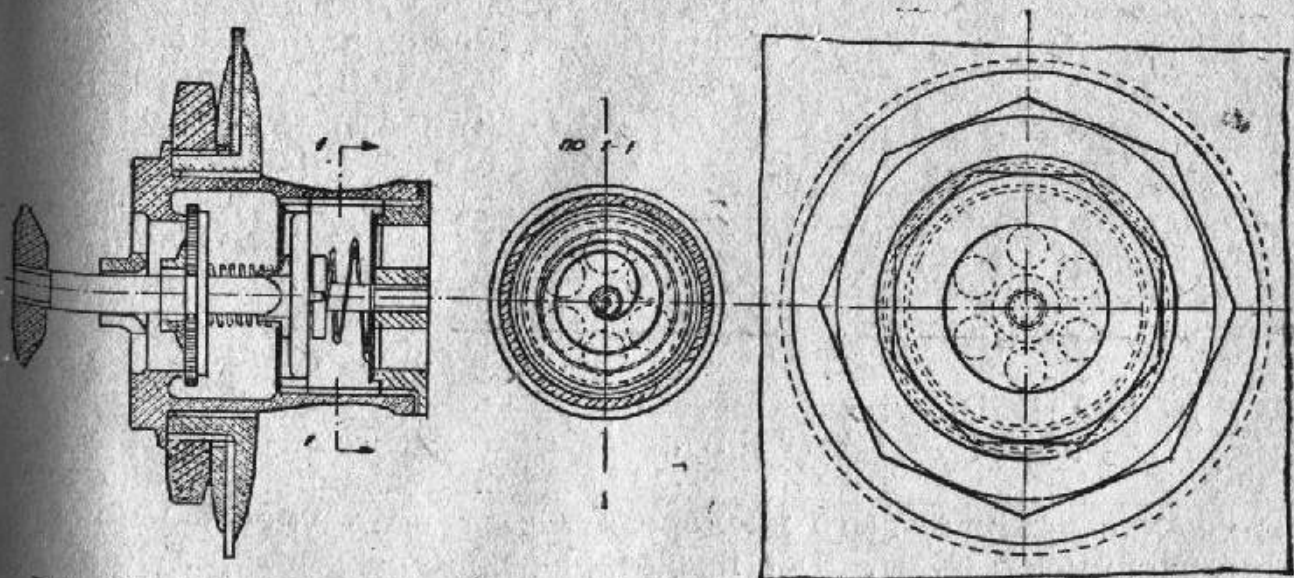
Избыточный клапан легочносилowego респиратора «ТП—1929 г.».
